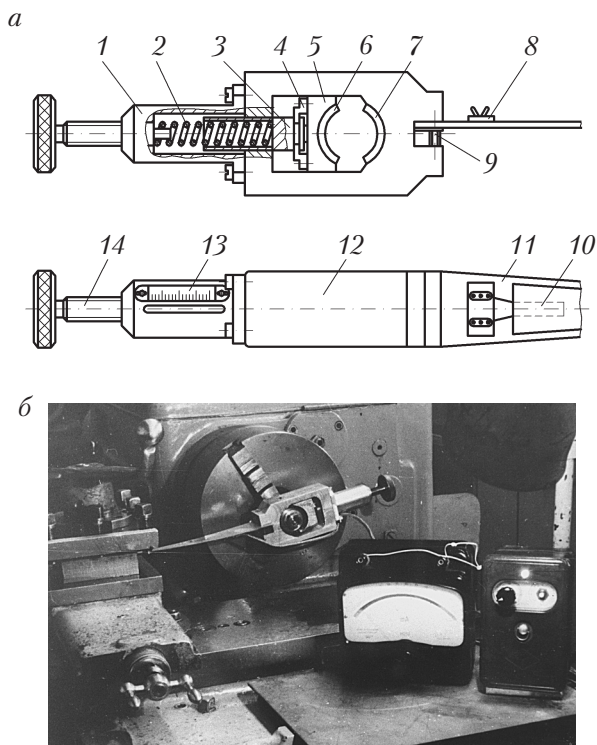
Тензометрическое устройство (а) и установка на базе станка мод. 1К62 (б) для испытания цилиндрических пар на фрикционные свойства
